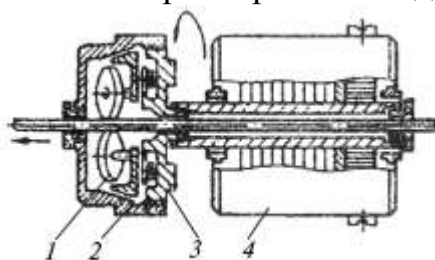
Безредукторный подающий механизм типа «Изаплан»:
